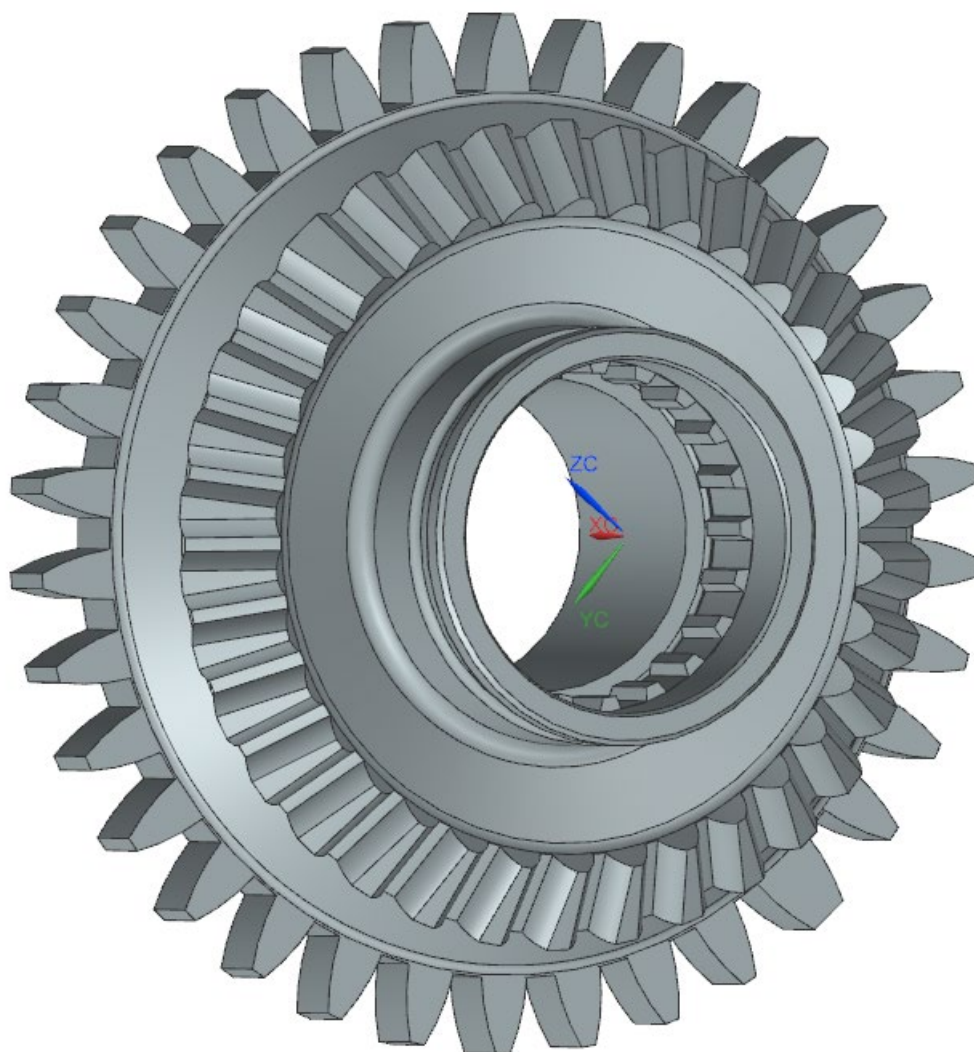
Тривимірна модель деталі шестерня конічна
